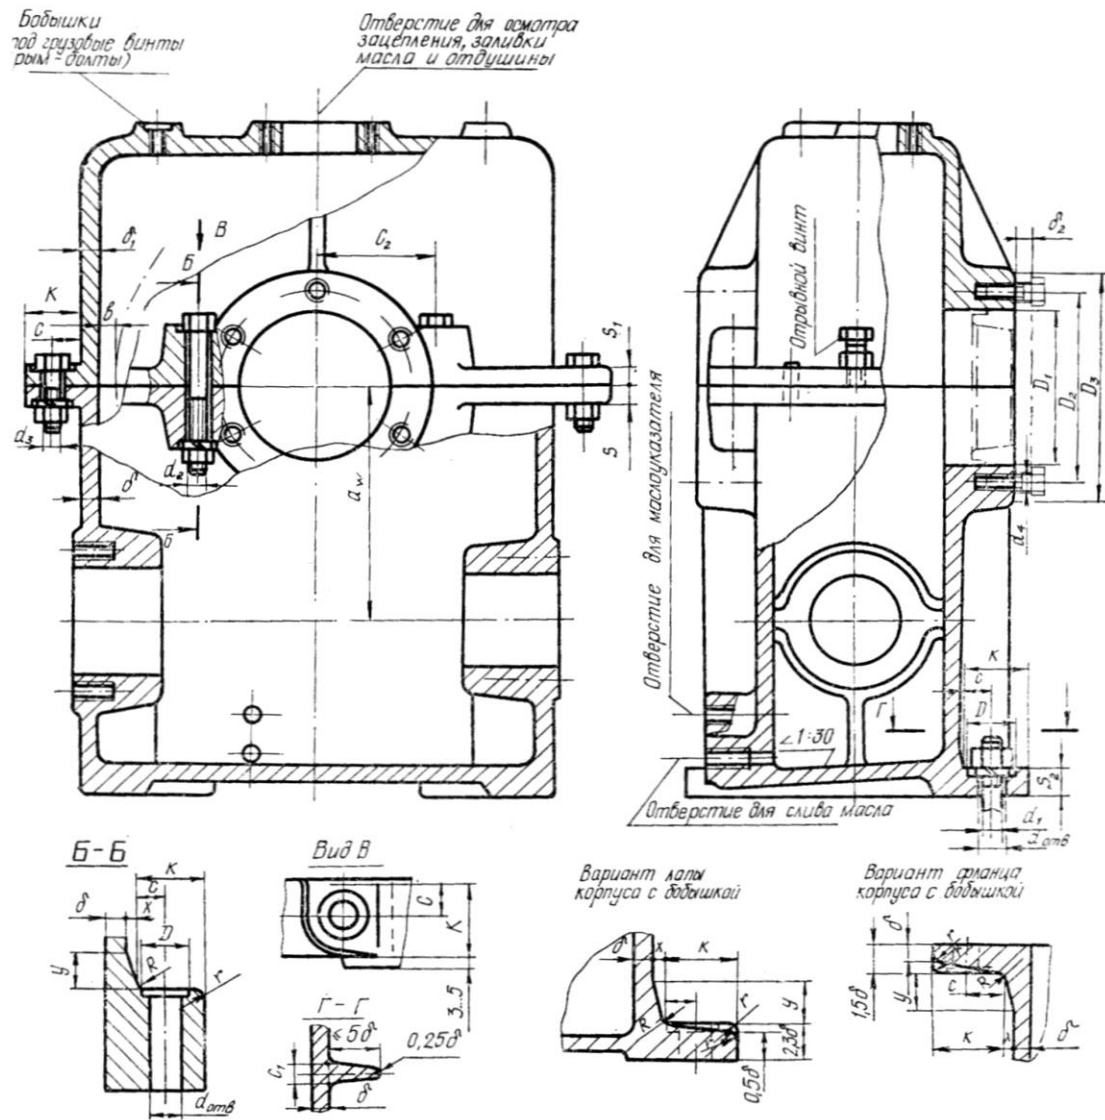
Конструктивні елементи корпусу і кришки черв'ячного редуктора
